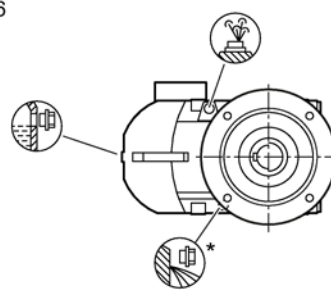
Монтажные положения для плоского редуктора F.F в исполнении с фланцем и F.Z с фланцем корпуса, типоразмер 39-189
